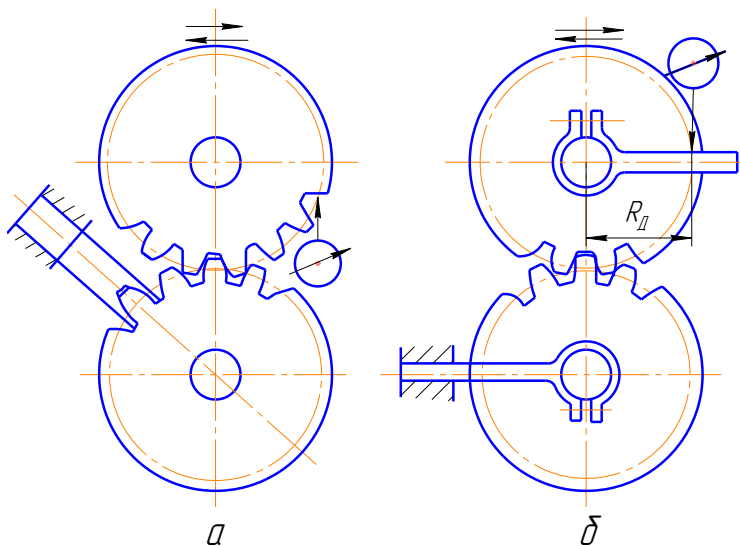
Схема контроля бокового зазора в зацеплении зубчатых колес
